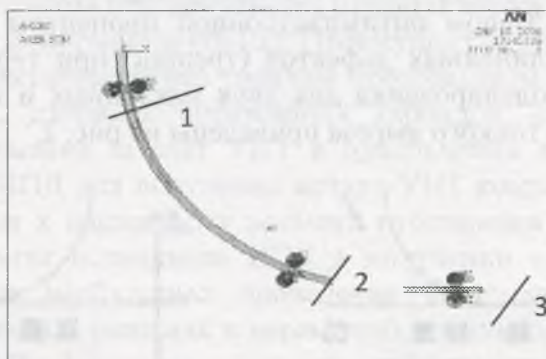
Схема прокатки заготовки на МНЛЗ: 1 – направляющие валки; 2,3 – тянущие валки.
